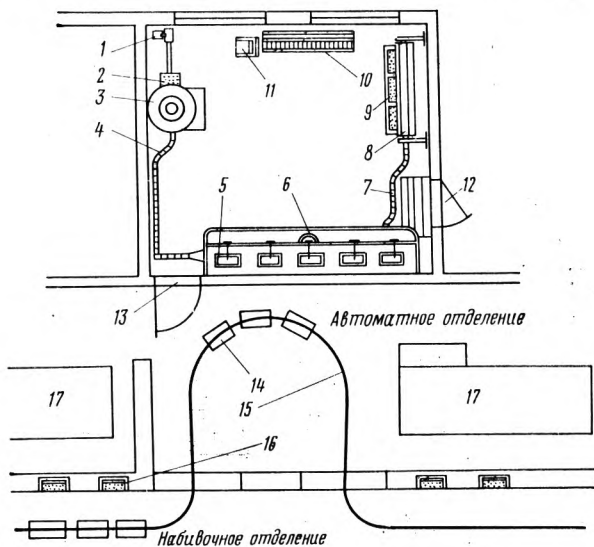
Схема размещения оборудования для укладки россыпи спичек:
